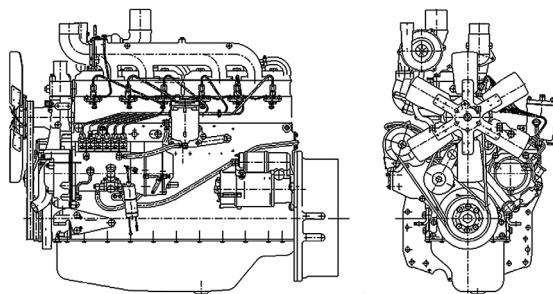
Двигатель внутреннего сгорания — сборочная единица 1-го порядка грузового автомобиля
